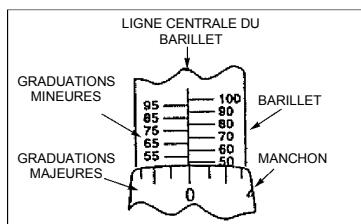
Réglage du couple de serrage à 50 Fig. 3 – Réglage du couple de serrage à 54
